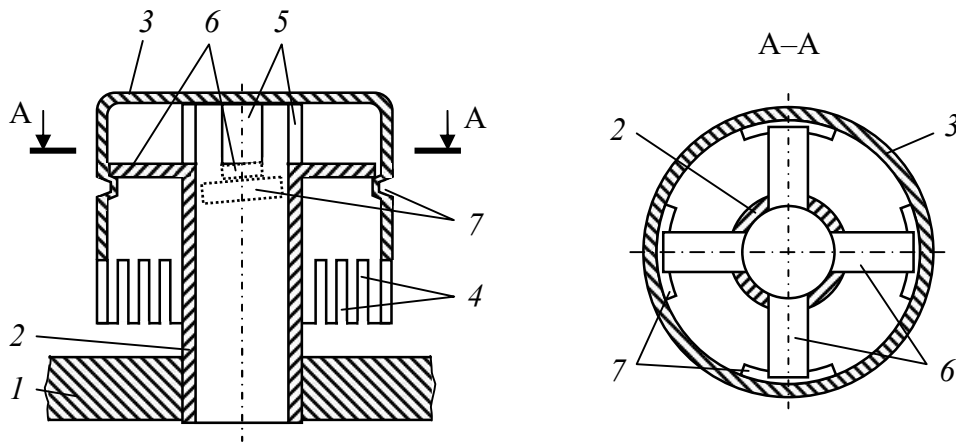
Конструкція ковпачкової тарілки згідно з пат. № UA108741U: 1 – полотно тарілки; 2 – газовий патрубок; 3 – ковпачок; 4 – прорізи ковпачка; 5 – прорізи газового патрубку; 6 – пелюстки газового патрубку; 7 – виступи ковпачка
